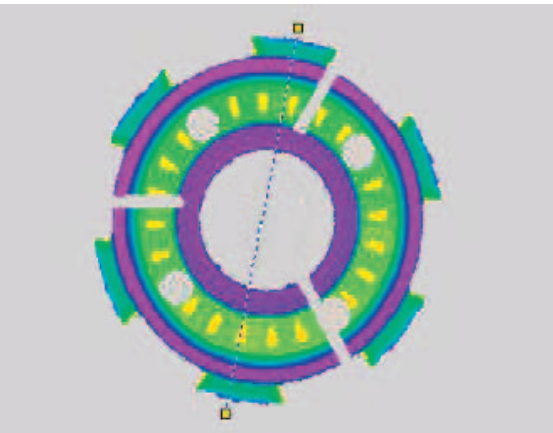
Stoßdämpfer-Bauteil mit mehreren Ringflächen
